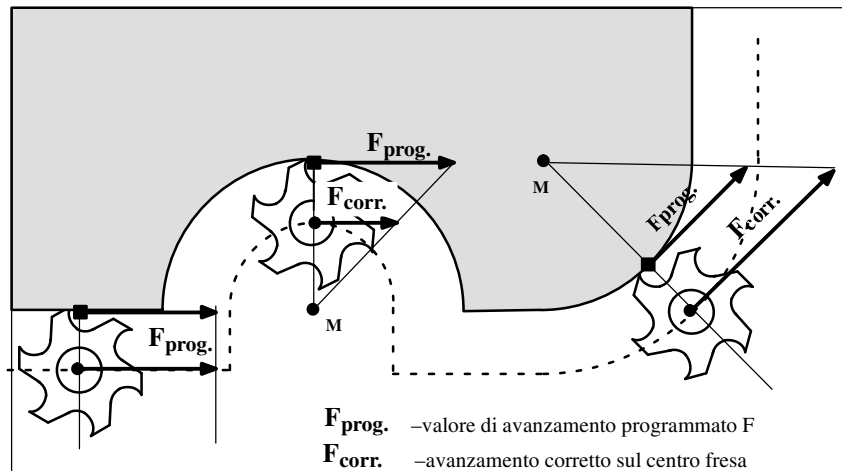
Correzione dell'avanzamento G901 nella lavorazione interna/esterna del cerchio
